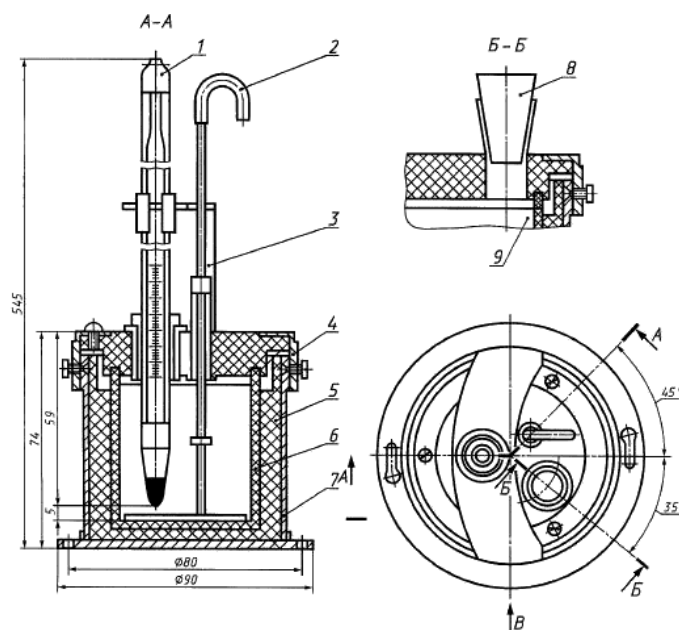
Влагометр: 1 - Термометр с муфтами; 2 - ручка мешалки; 3 - ручка крышки; 4- крышка; 5- термоизоляционный стакан; 6- стакан влагометра; 7- корпус; 8- пробка; 9-уплотнительное кольцо.
